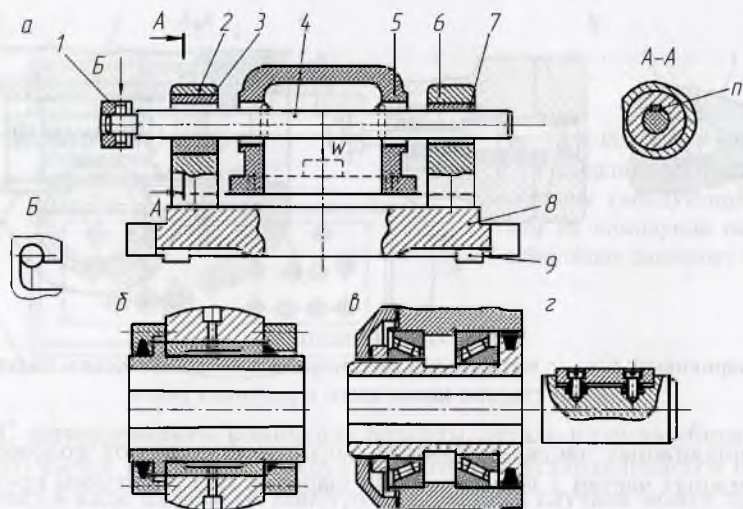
Схемы расточного приспособления (а), вращающихся на подшипниках скольжения (б) и качения (в) направляющих втулок и конца расточной борштанги (г) с плавающей шпонкой
